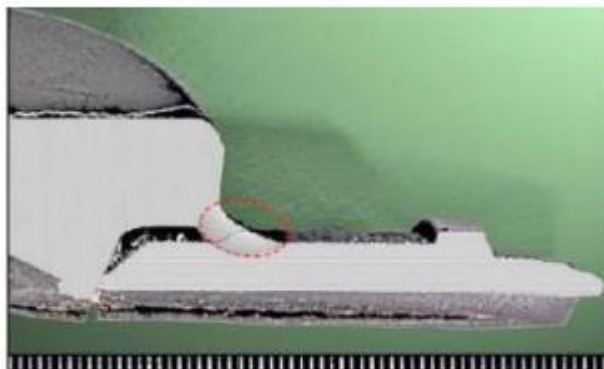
Сквозная трещина в сварном шве, сечение вдоль оси штуцера
